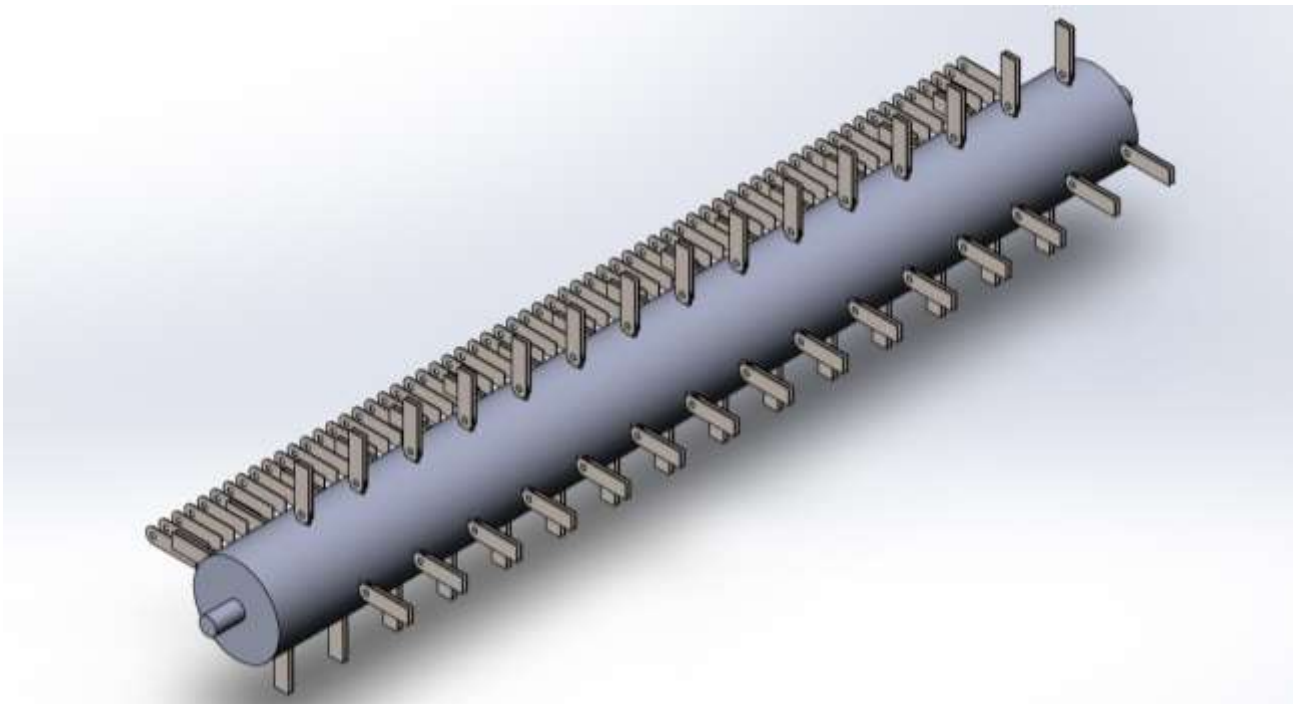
Загальний вигляд ножового барабана з шарнірно-закріпленими ножами
